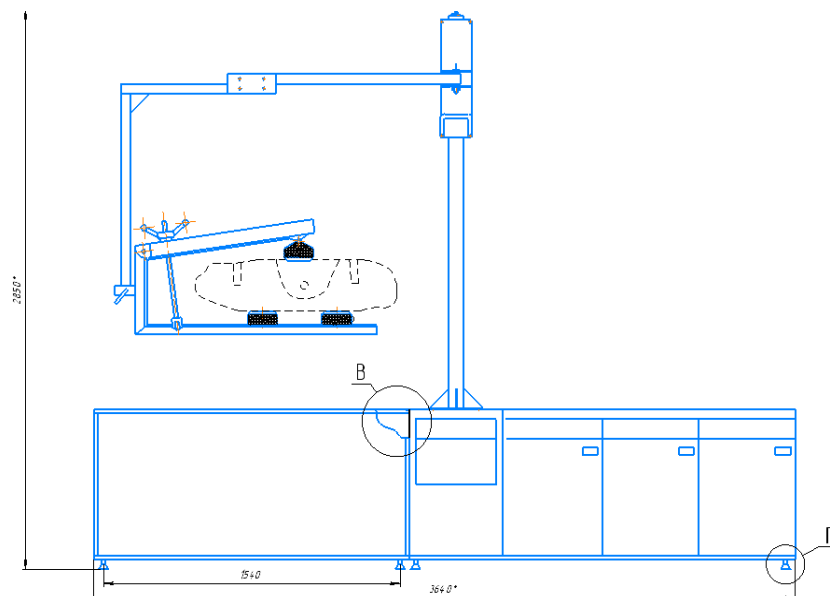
Стенд для проверки герметичности и ремонта радиатора и топливного бака
